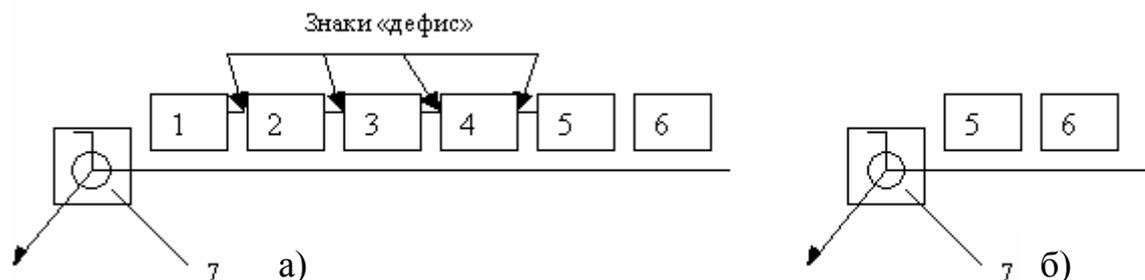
Структура условного обозначения сварного шва
